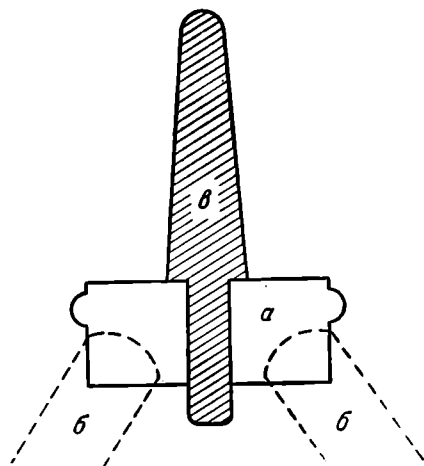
Приспособление для установки буссоли на штатив фотоаппарата
